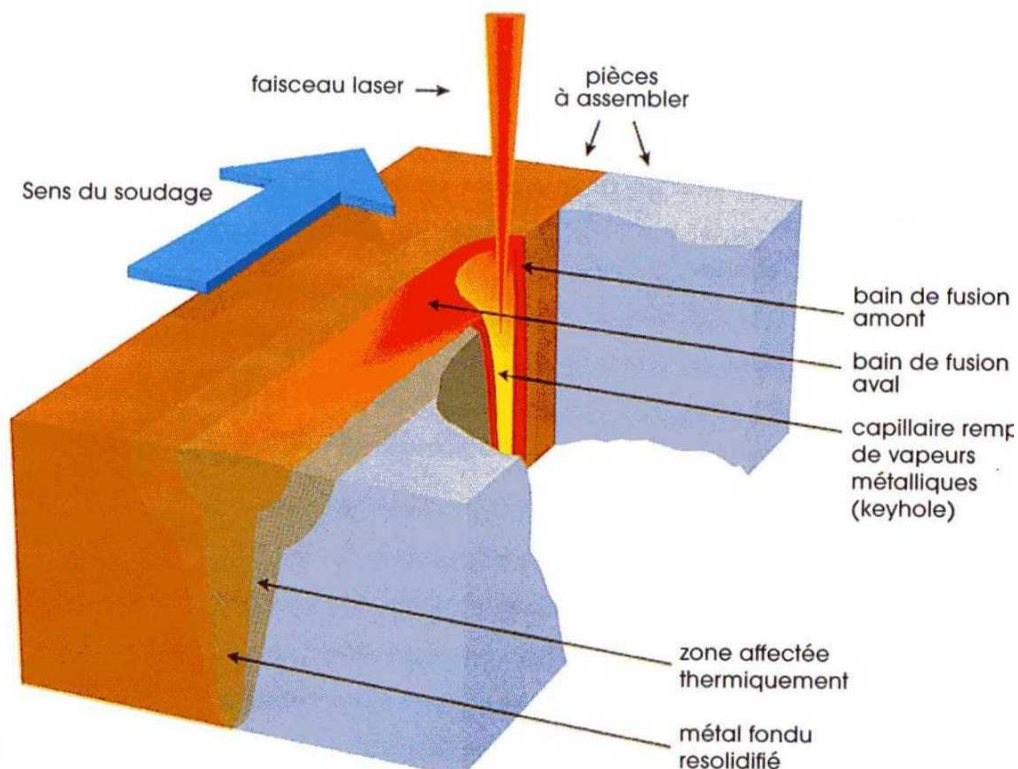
Schéma de soudage laser continu en mode keyhole
